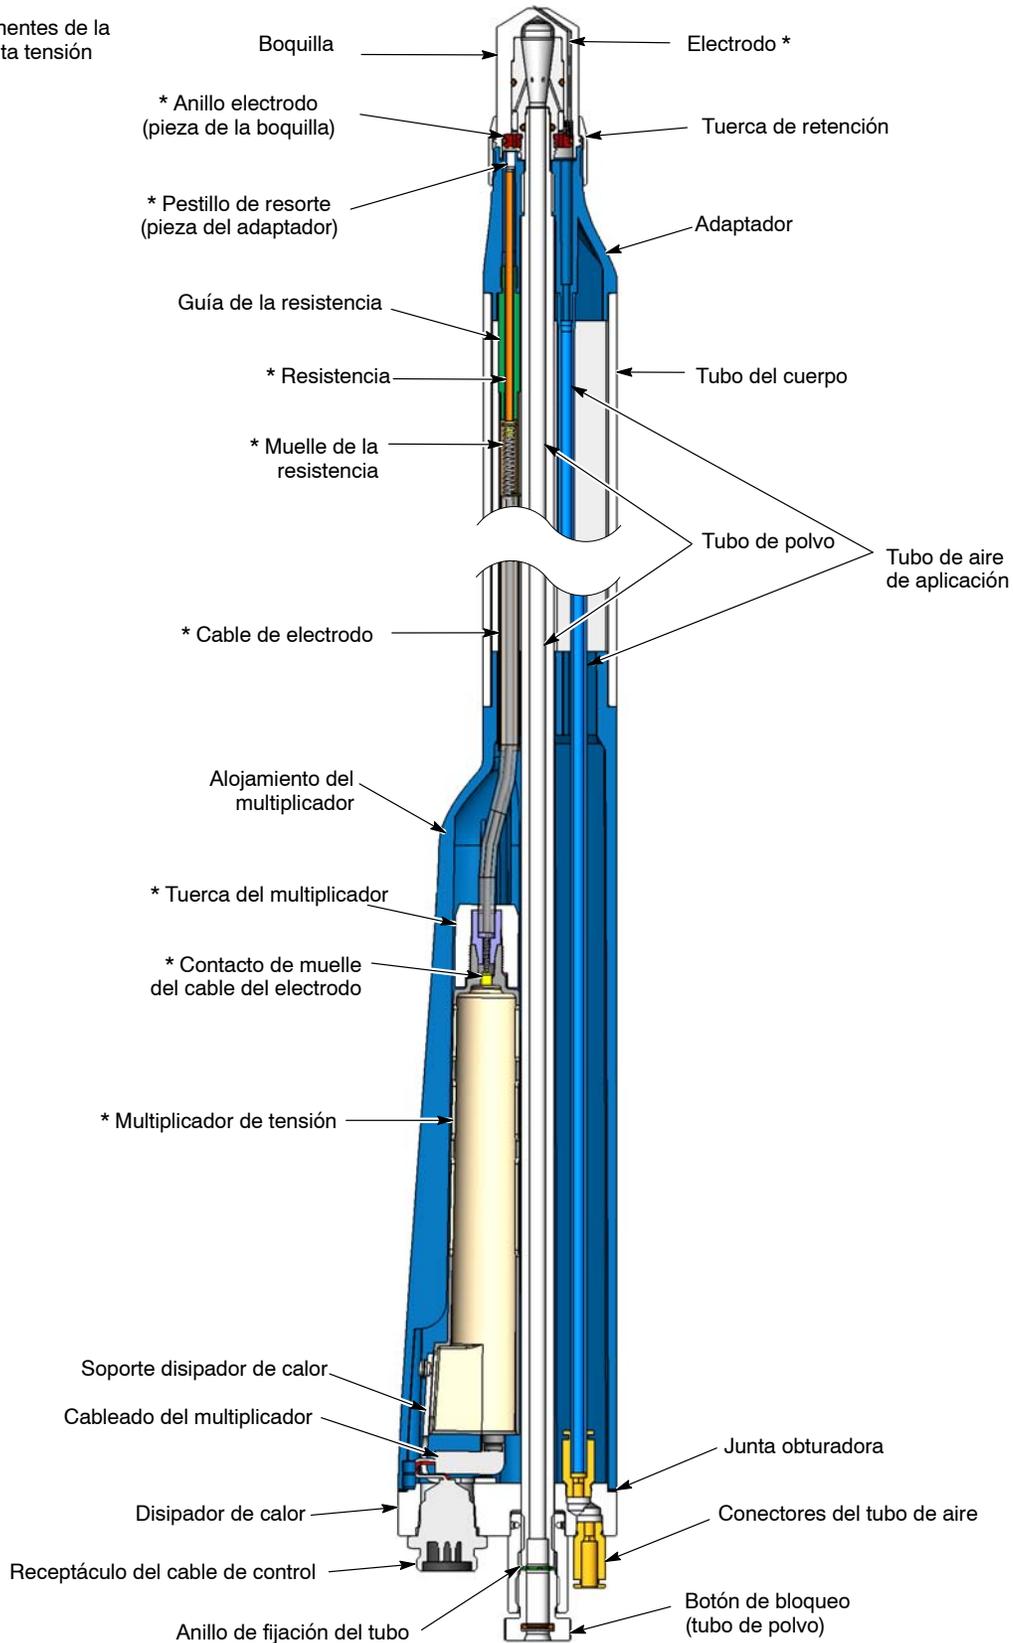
Vista transversal – Componentes y montaje de la pistola de montaje en tubo
